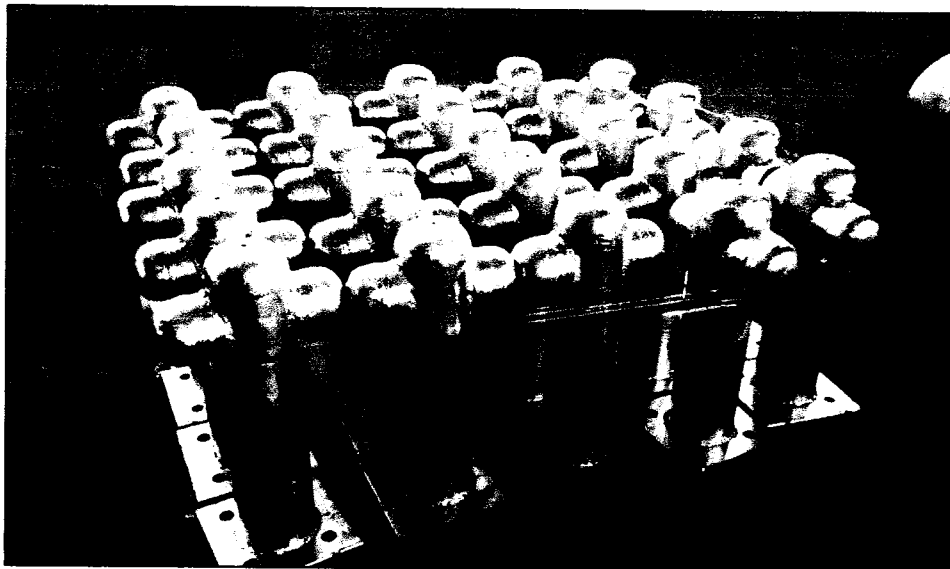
Bitas de Anclaje Galvanizadas con recubrimiento de Zinc en Caliente.
